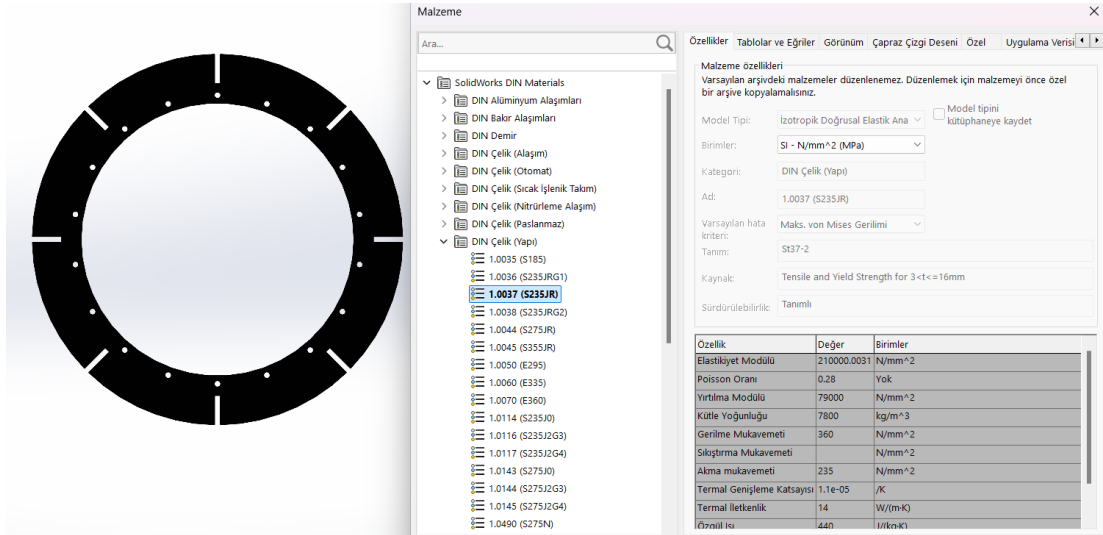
Step motor tutucusunun malzemesinin tanımlanması
